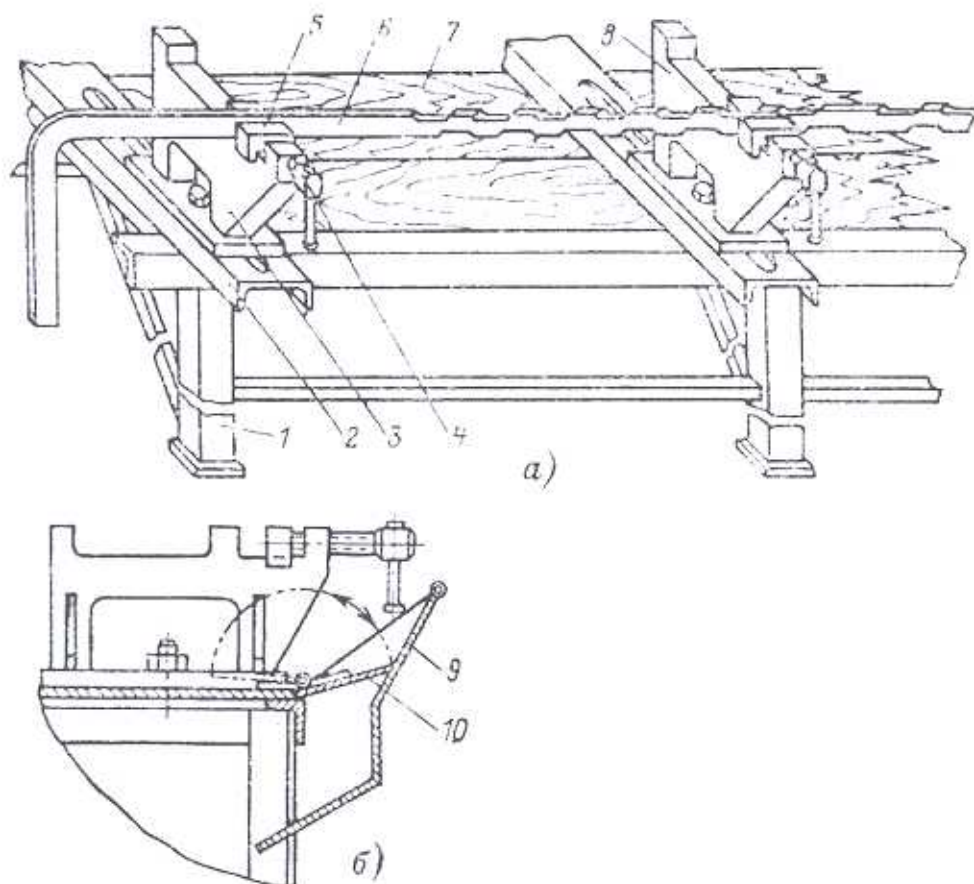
Стол для опиловки витков, схема, детали конструкции:
